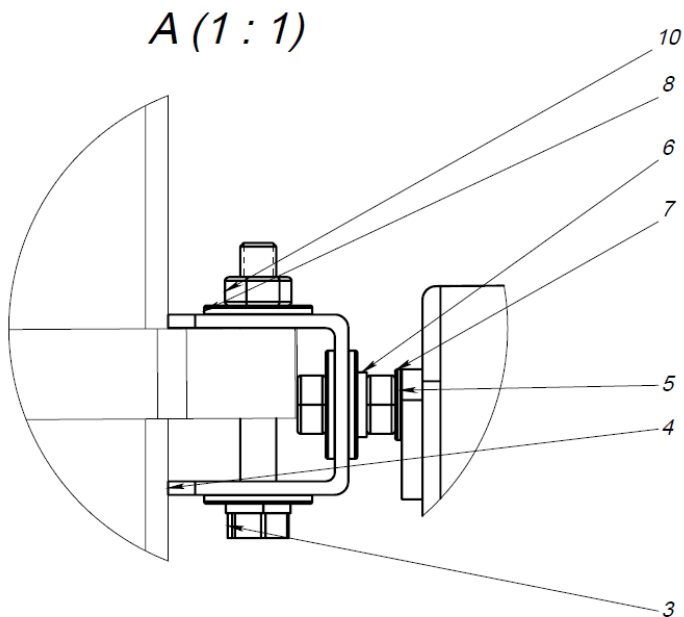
Увеличенный вид крепления к несущей конструкции.
